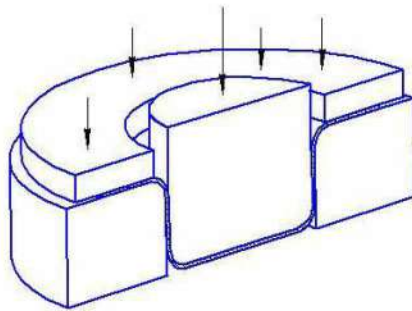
Схема штампу для витягування із жорсткою плитою, що притискає
